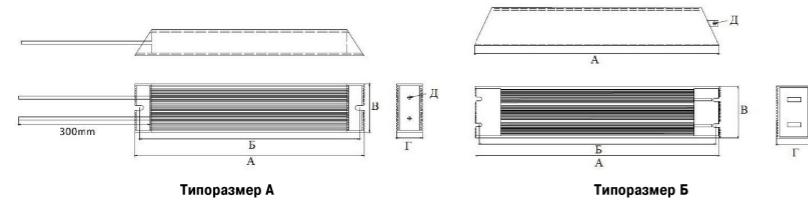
Габаритно-установочный чертеж резисторов серии РБ3
